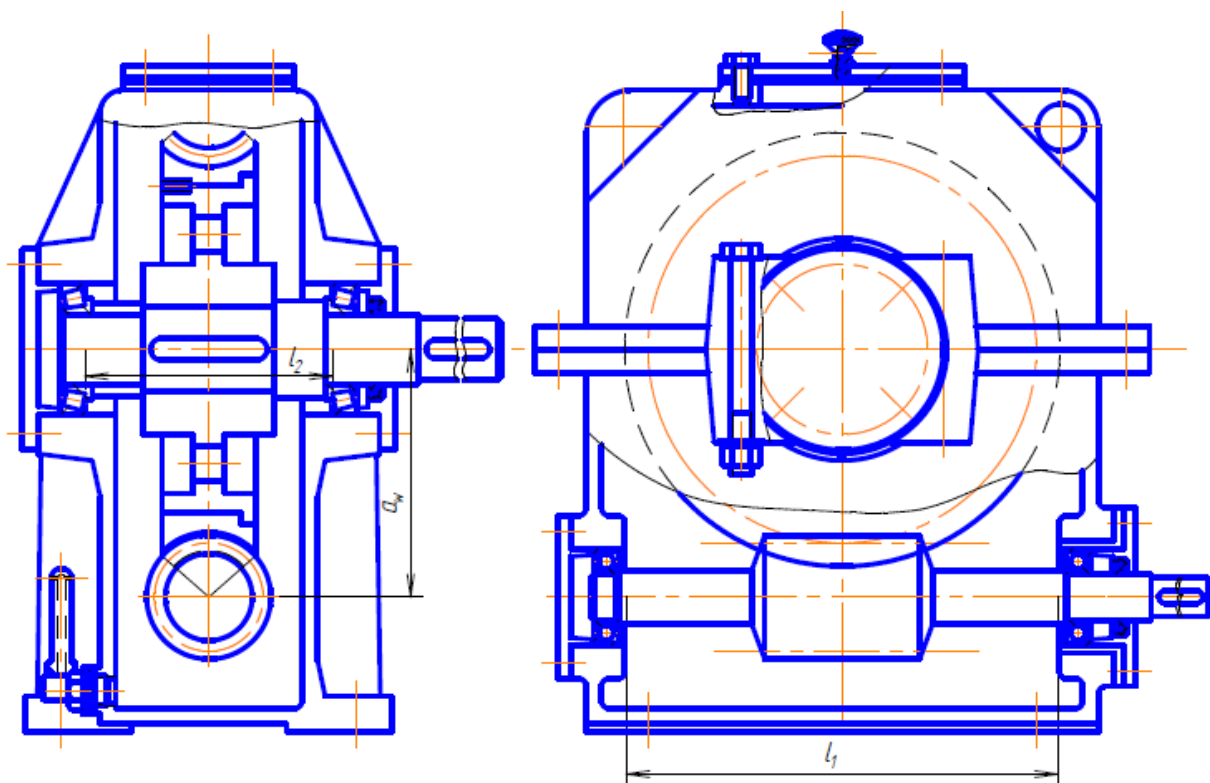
Приклад конструктивної компоновки черв'ячного редуктора
